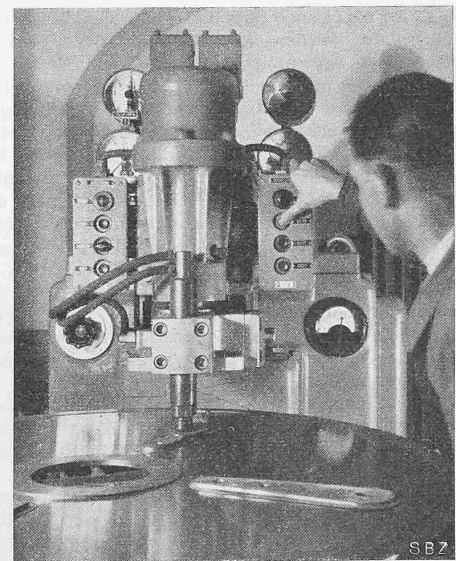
Stirnseite des Schweissarmes einer Maschine für 10 verschiedene Schweissprogramme
